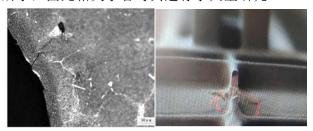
熔模铸造 K424 薄壁铸件裂纹缺陷^[15] Fig.3-2 Crack defects of K424 thin-walled castings formed by investment casting process[15]
